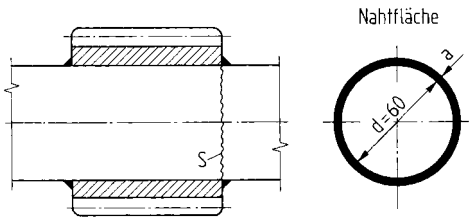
Aufgeschweißtes Ritzel
